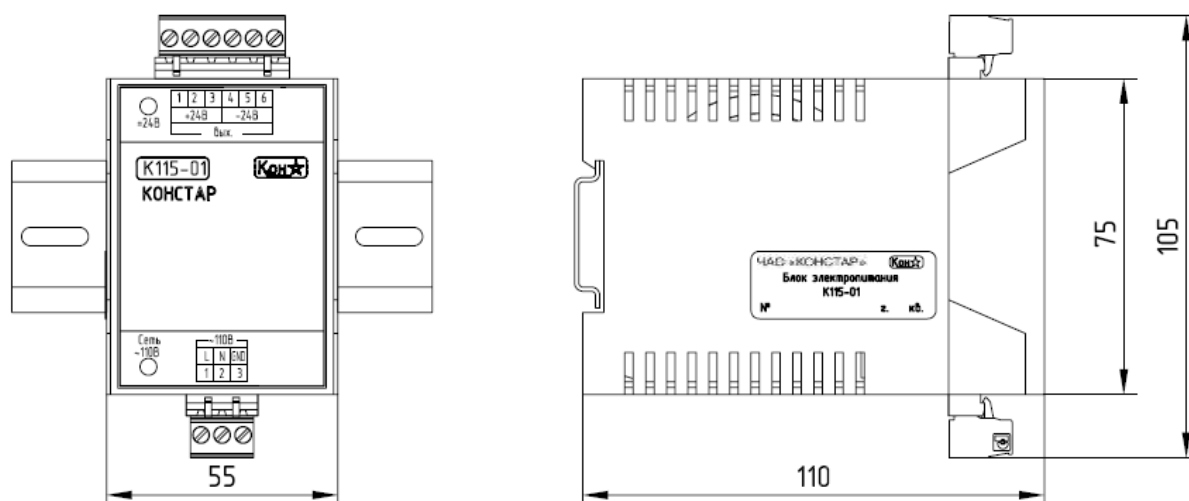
Габаритные и установочные размеры блока питания K115
